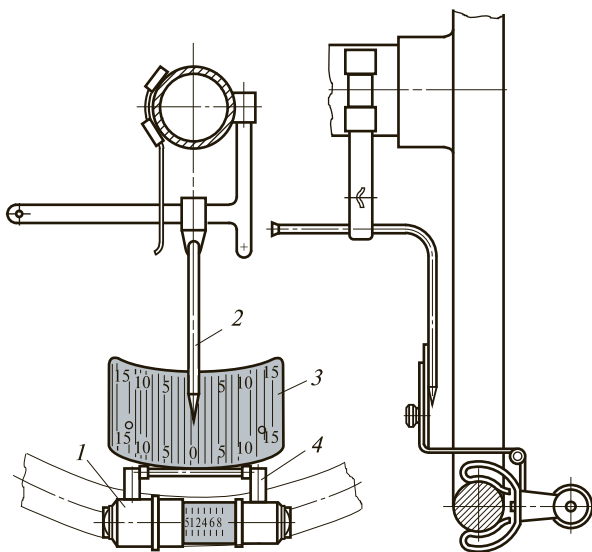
Прибор К-187 для проверки рулевого управления:
